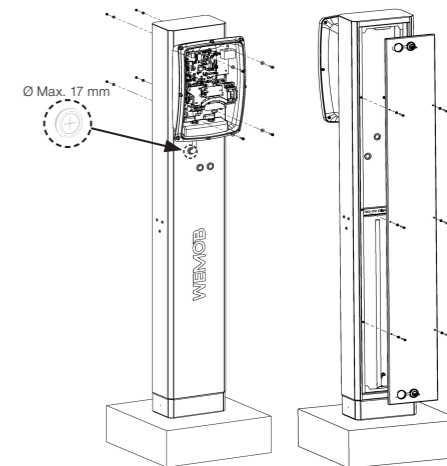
Exemplo fixação da estação WALL G2 no totem
